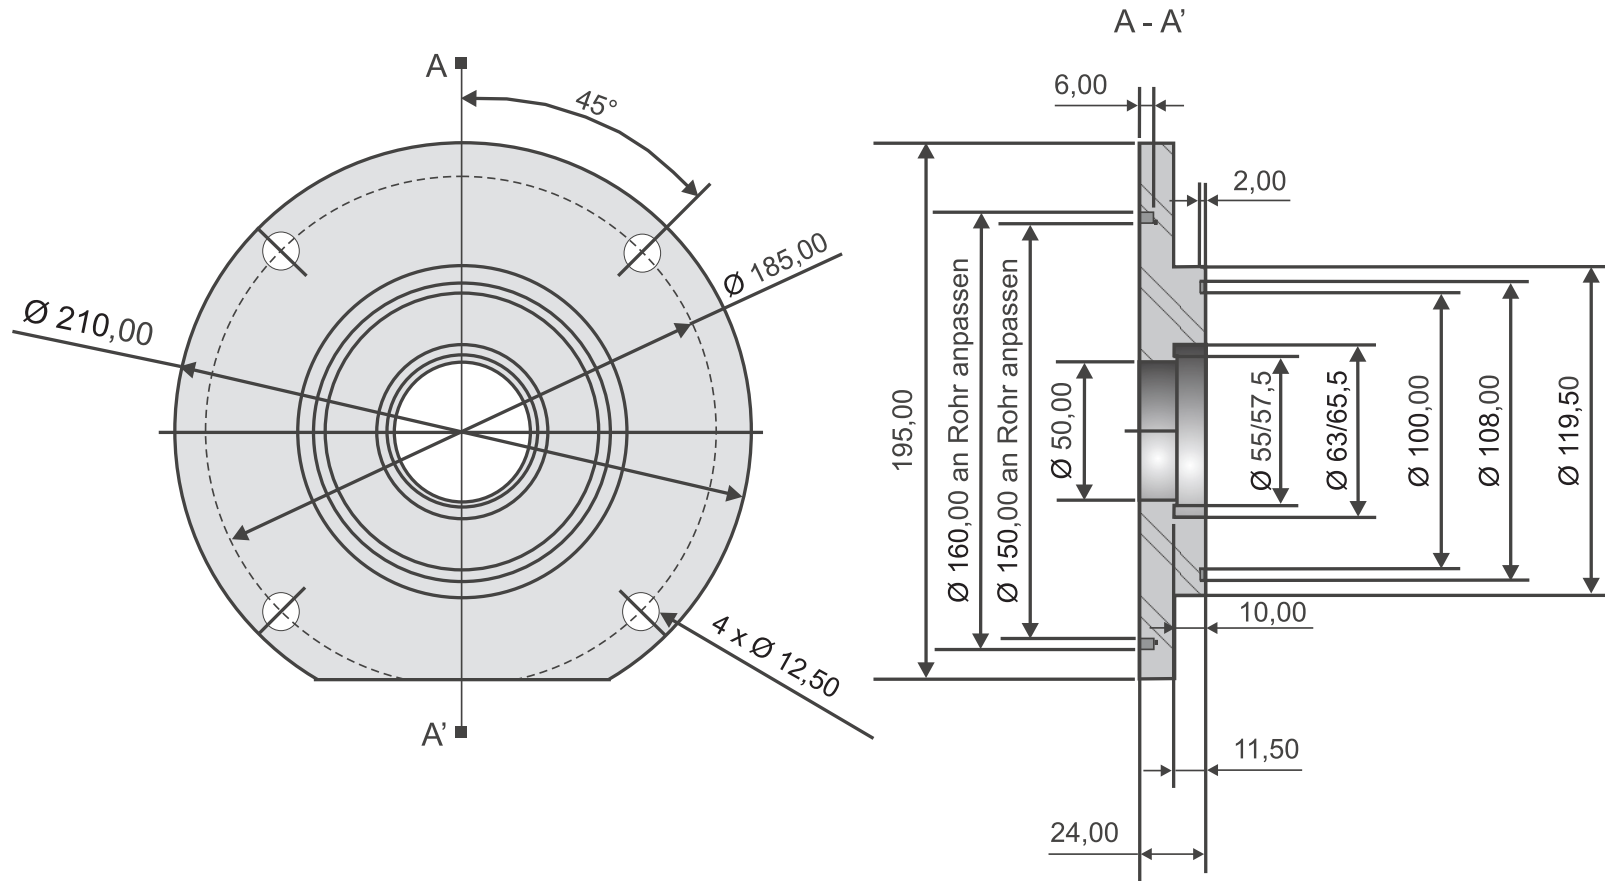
Technische Konstruktionspläne für V5A-Stahlzelle. Untere Mittelscheibe, in welche Gesteinsprobe platziert wird. Für Gesteinsprobe Negev, weiß \emptyset von 63 mm; Negev, grau \emptyset 65,5 mm.
